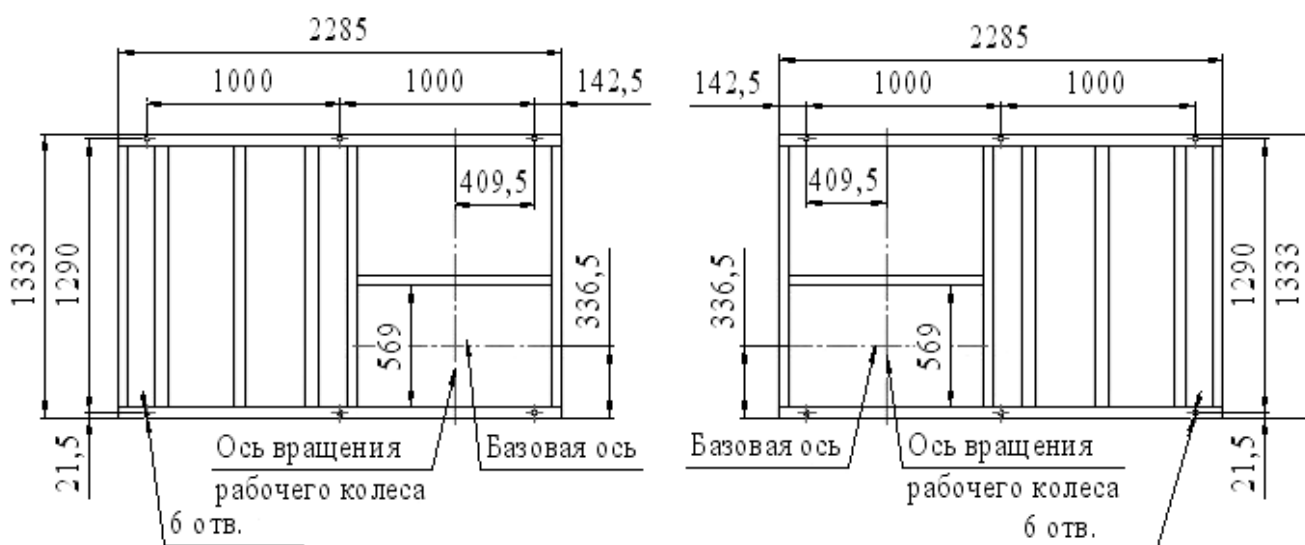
Вентиляторы ВПИ-PRU-1000. Установочные размеры.
